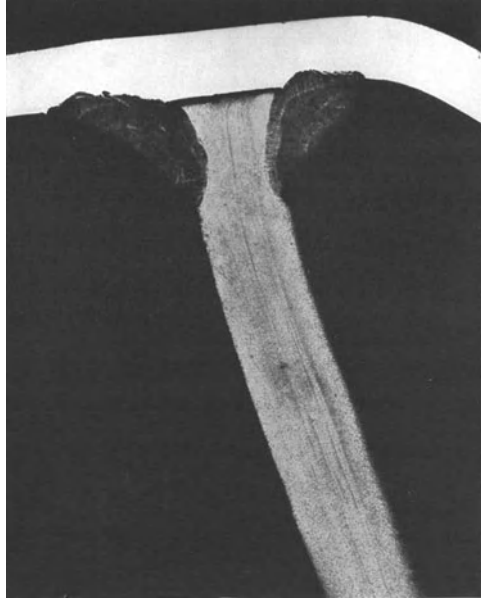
Schnitt durch eine Eckenschweißung von Flacheisen. Verschweißung von rostfreiem mit C-Stahl.
